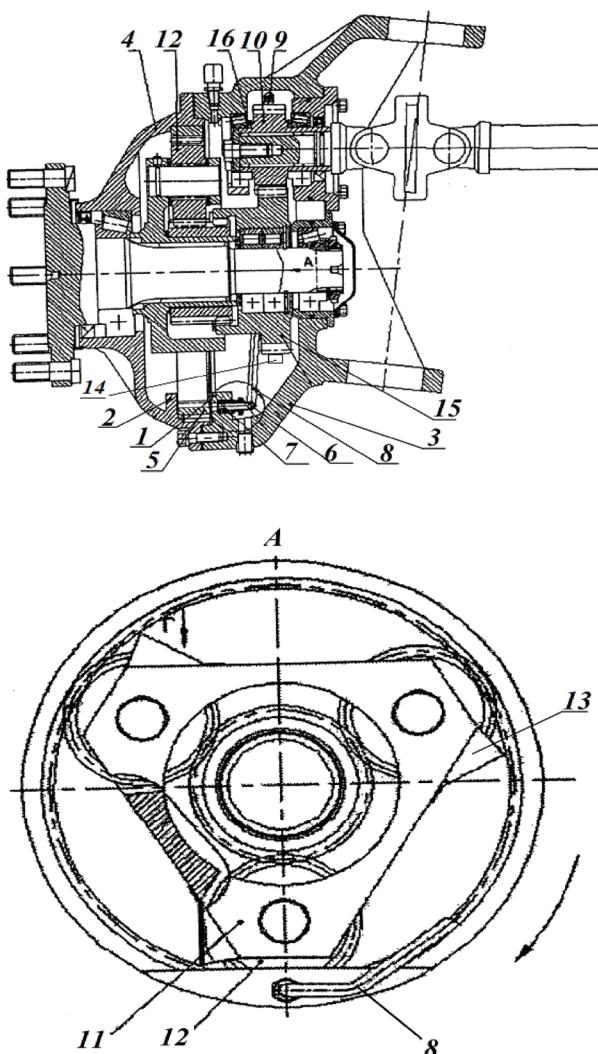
Планетарно-цилиндрический бортовой редуктор мобильной машины с насосом: 1, 2 – стенки, 3 – корпус редуктора, 4 – крышка, 5, 10, 15 – шестерни, 6 – штуцер, 7 – уплотнительный конус, 8 – трубопровод, 9 – форсунка, 11 – водило, 12 – сателлит, 13 – пластина, 14 – контрольная пробка, 16 – подшипник
